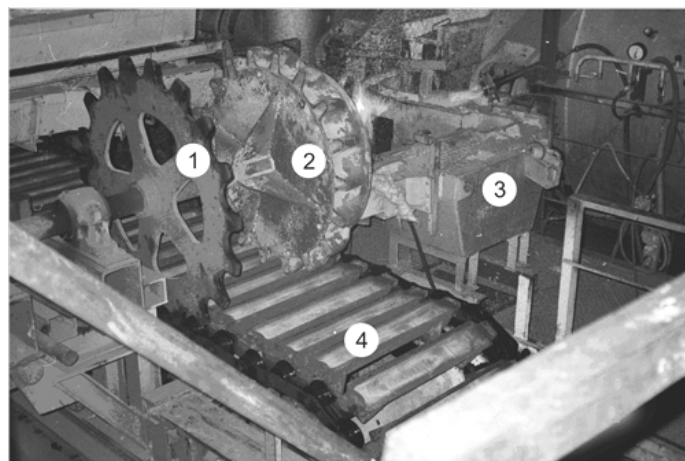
Устройство очистки и безокислительной разливки металла в изложницы: 1 – синхронизатор; 2 – блок безокислительного розлива; 3 – блок фильтрования; 4 – конвейер разливочный
